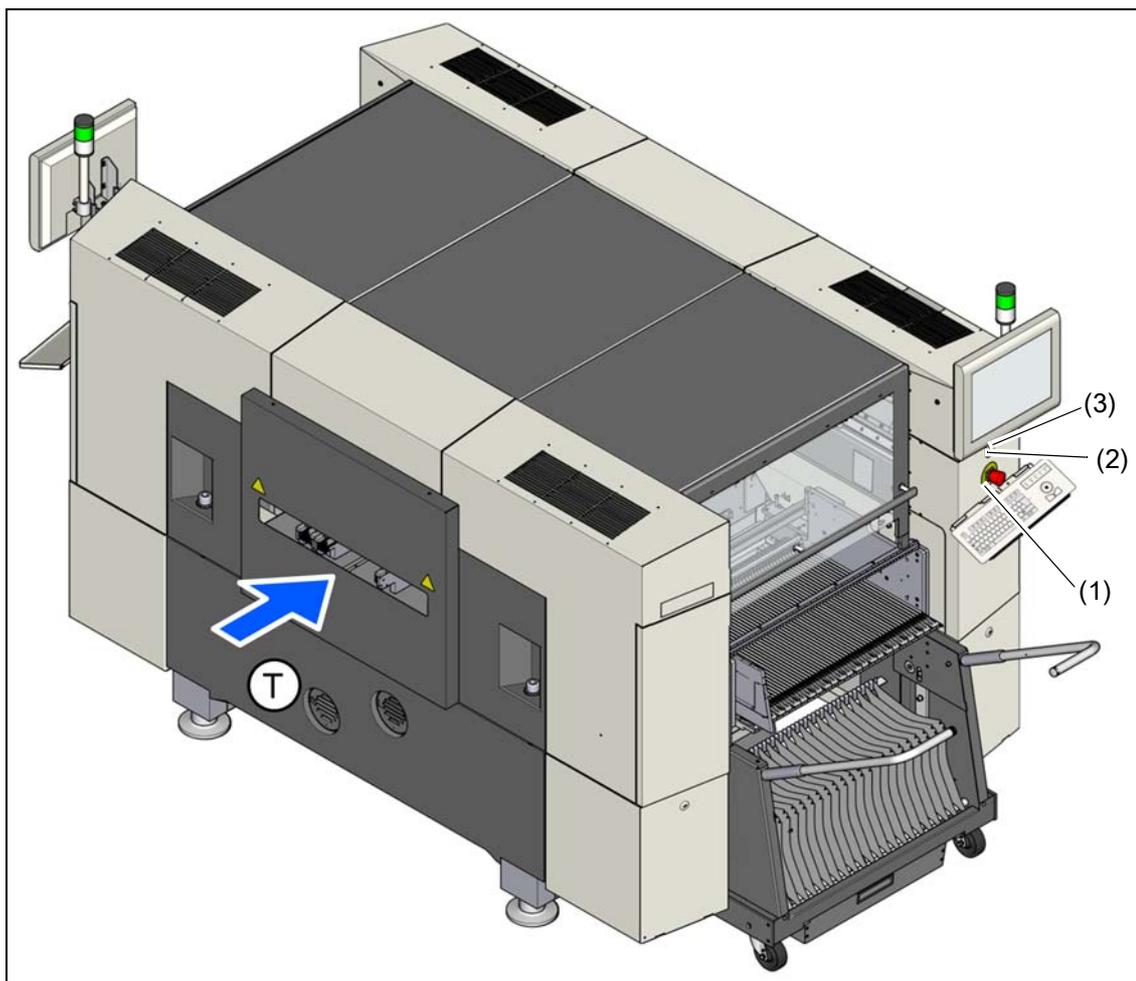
4 开关和按钮的位置 - 从 PCB 输入侧观察
